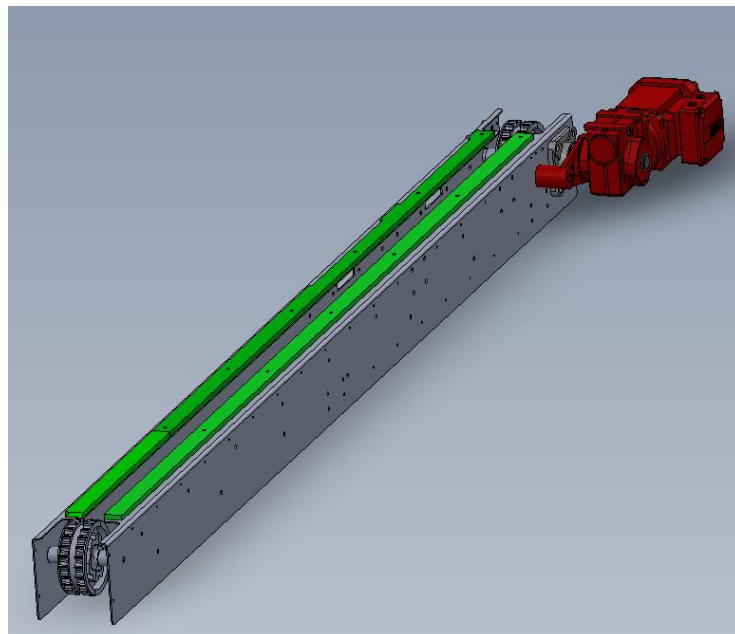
Πρόσδεση κινητήρα σε exploded view
